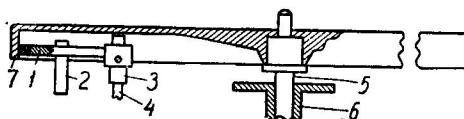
Схема редуктора универсального электропроигрывателя: 1 — ролик; 2 — ось ролика; 3 — насадка; 4 — вал электродвигателя; 5 — вал диска; 6 — подшипник диска; 7 — диск проигрывателя
